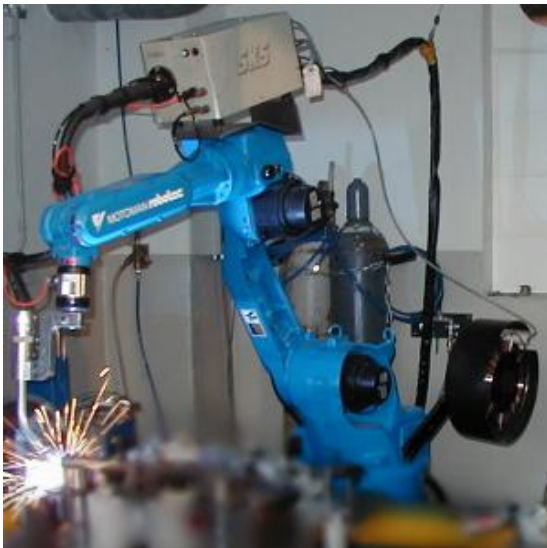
Gelenkarmroboter mit Schweißbrenner
